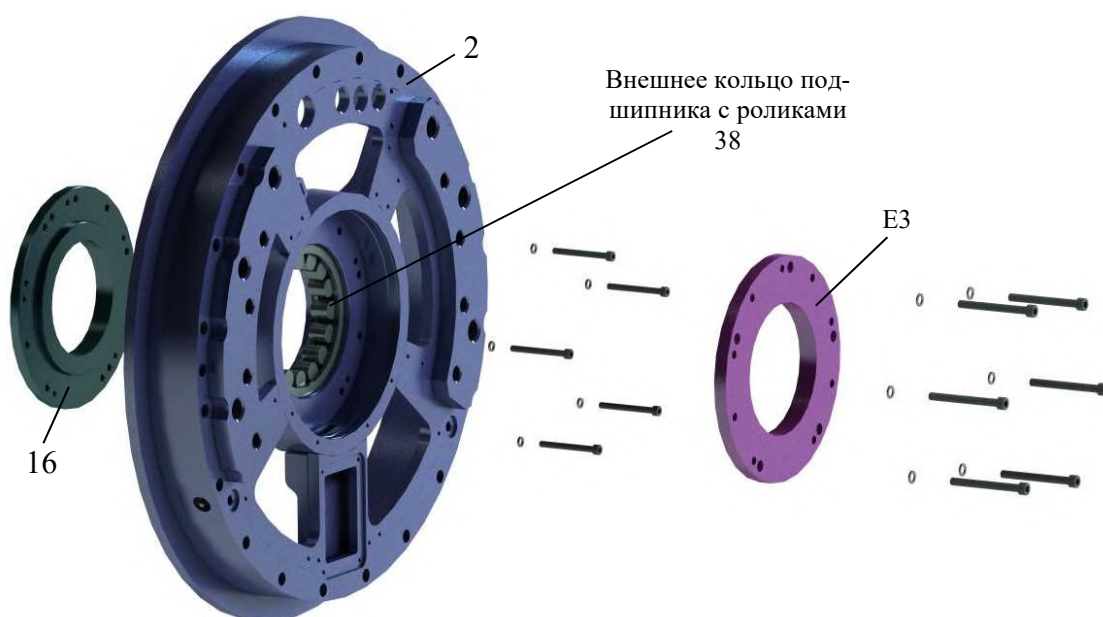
Установка внутреннего лабиринта в подшипниковый щит со стороны тормоза
